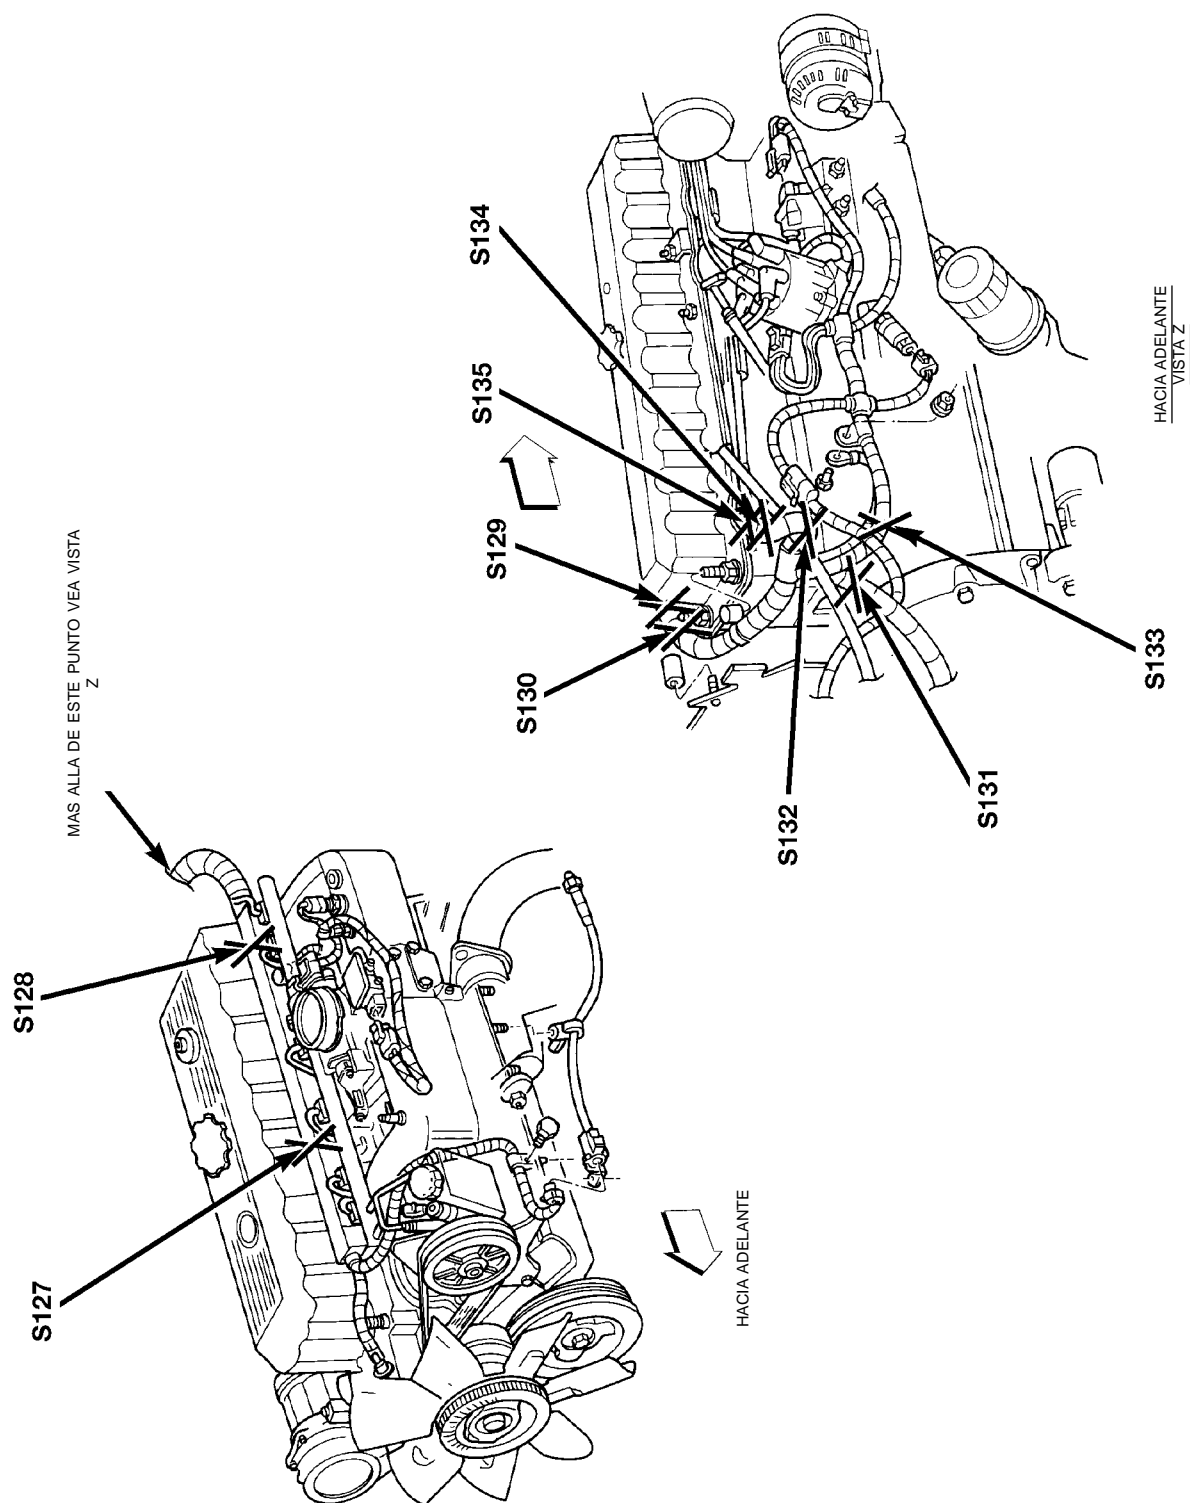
Empalmes del cableado del motor—Motor 4.0L
